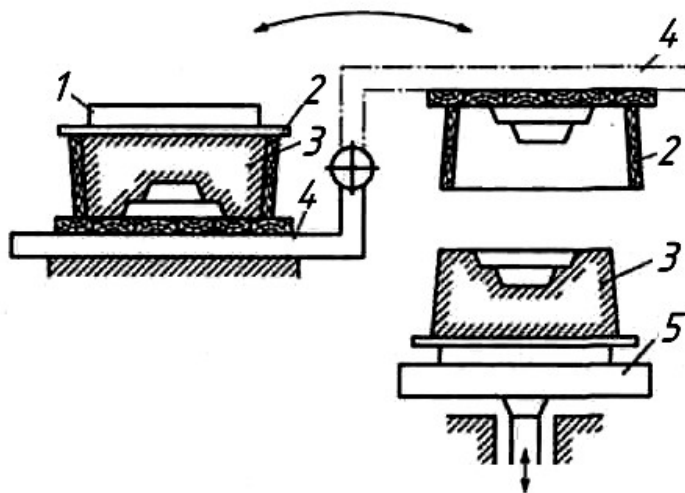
Схема извлечения средних стержней с встряхивающих машин с поворотно-вытяжными механизмами: 1 – сушильная плита; 2 – стержневой ящик; 3 – стержень; 4 – поворотный стол; 5 – приемный (вытяжной) стол
